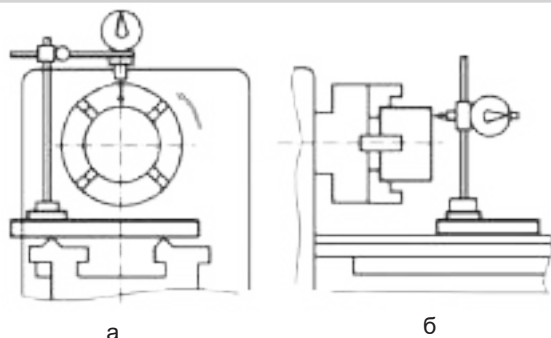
Закріплення та вивірка заготовки індикатором: *а* — індикатор по зовнішній поверхні; *б* — індикатор по торцю
